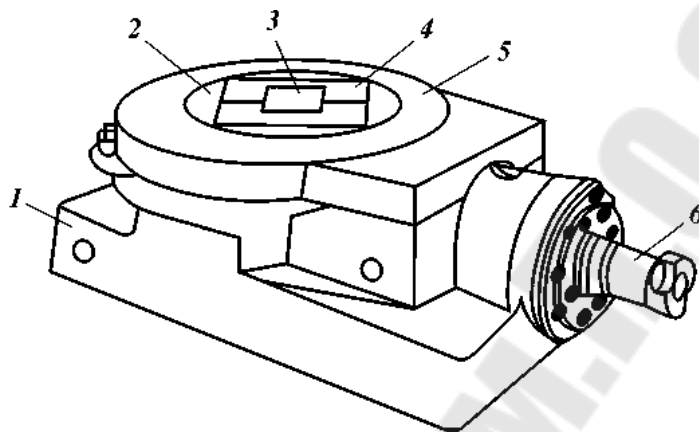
Схема ротора буровой установки: 1 – станина; 2 – стол; 3 – отверстие; 4 – вкладыши; 5 – рифленый кожух; 6 – вал привода
